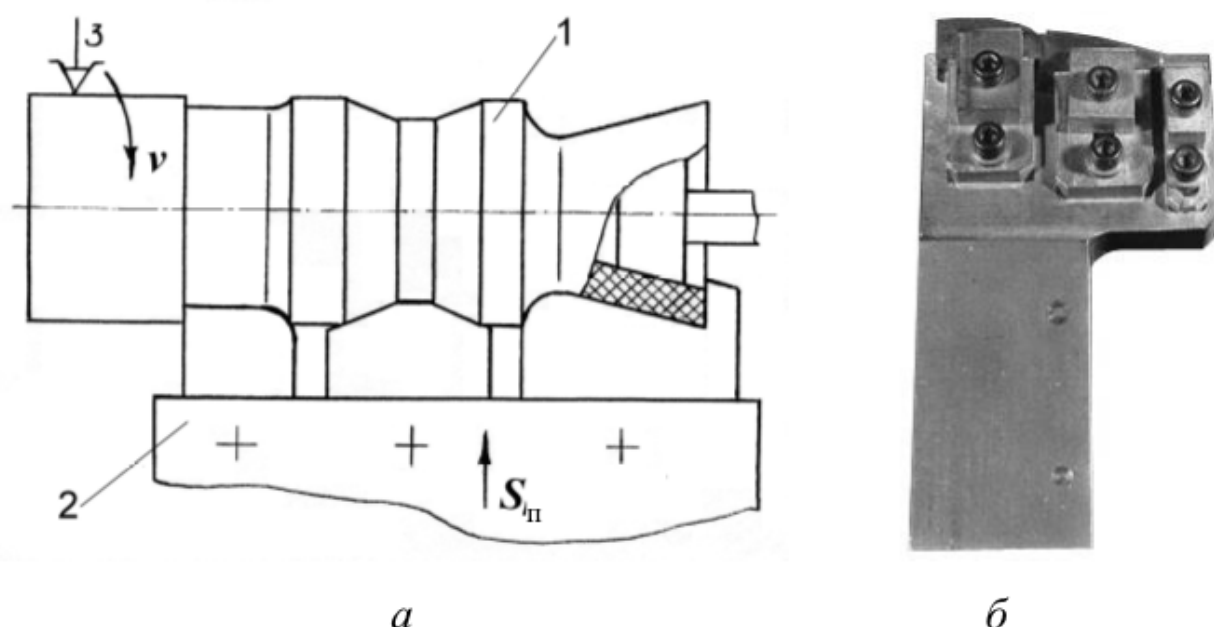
Схема обработки резанием с применением МШС (а) и общий вид широколезвийного резца — резцового блока (б):
